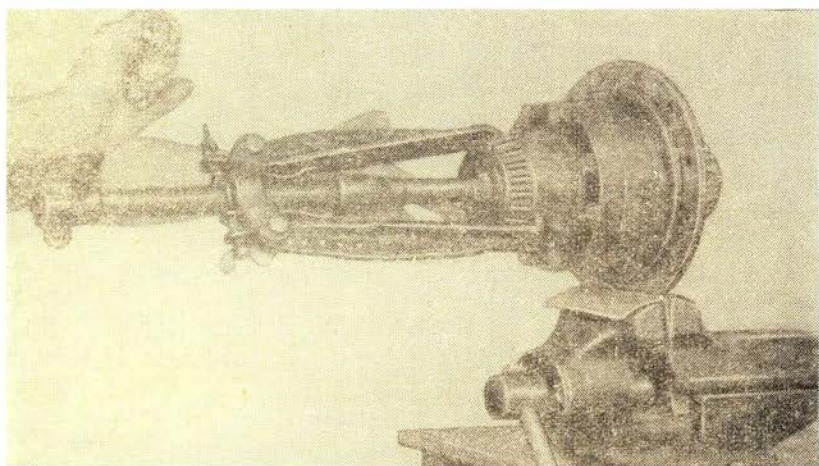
Снятие подшипника с правой чашки коробки сателлитов
